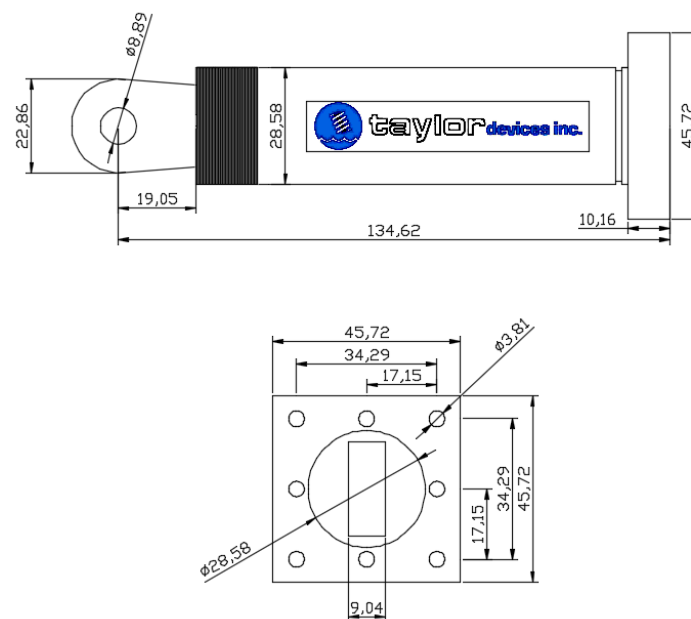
Dimensiones de disipador F= 440 KPI por taylordevices.com, 2017
